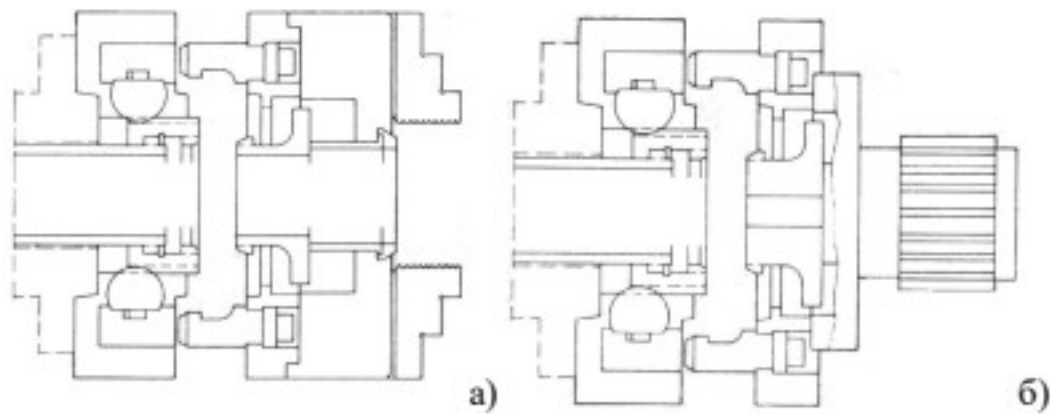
Пристрій зміни фірми «Gamet»: а - затискного патрона; б - розтискної оправки
